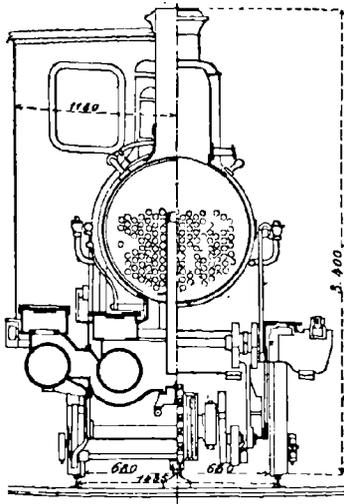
Machine de la ligne de Lehesten à Oertelsbruch.
